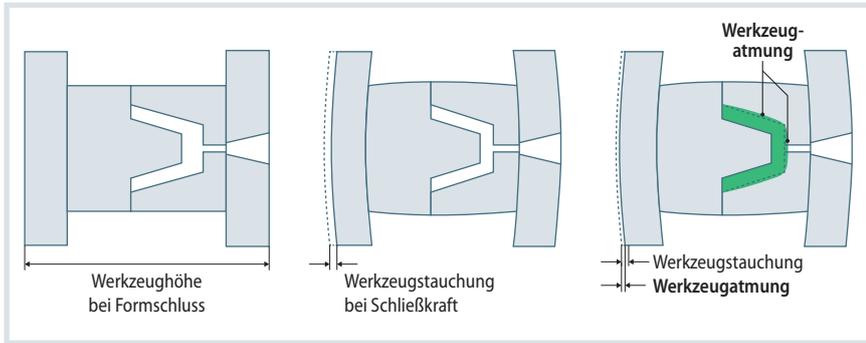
Werkzeugatmung: Das Werkzeug wird durch den Aufbau der Schließkraft gestaucht. Im Füllvorgang erzeugt das entstehende Formteil eine Auftriebskraft, die der Stauchung entgegenwirkt. Die Auftriebskraft ist proportional zum Werkzeuginnendruck und zur projizierten Fläche
